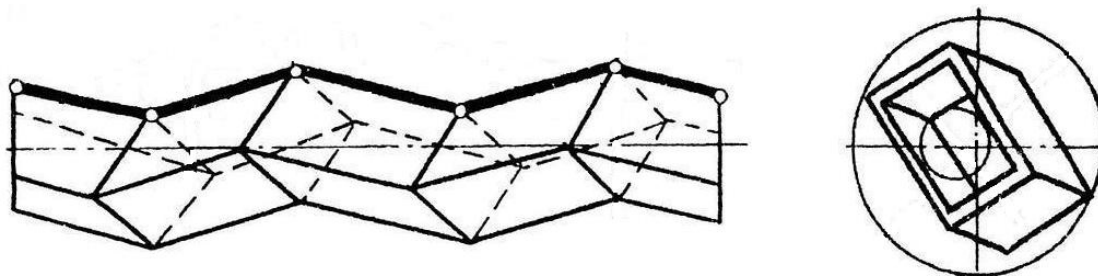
Релятивный цилиндрический винтовой барабан РЦ 1.1.б
